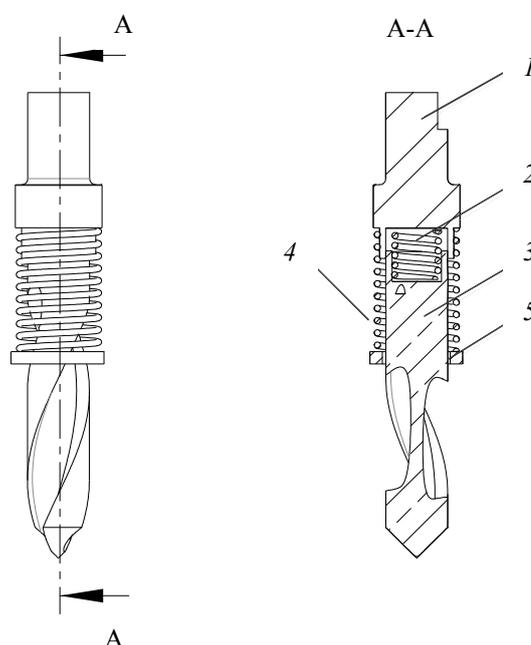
Устройство сверла сборного для сверления ЛДСтП:
